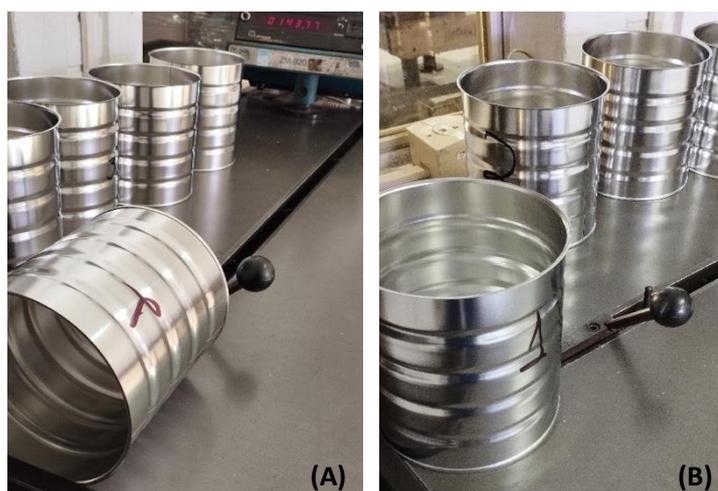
Latas para análise dimensional numeradas de 1 a 4 (A). Cortes em 3 pontos (B): A lado direito, B lado esquerdo e C paralelo a solda da lata
